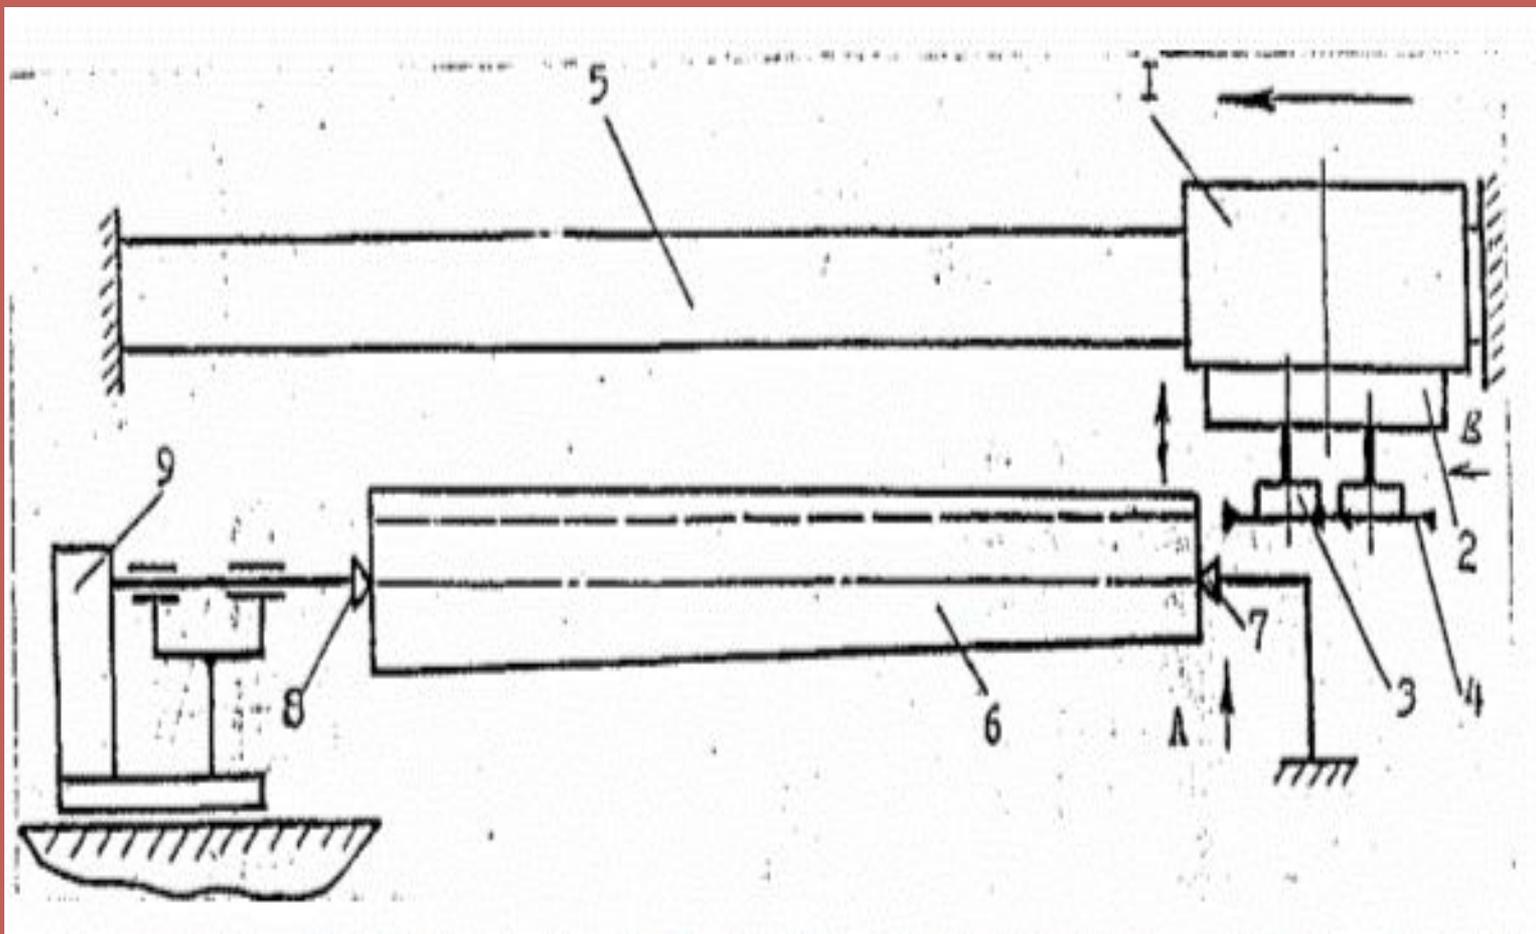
Вид А ОЦ : 1- каретка: 2- суппорт: 3- фреза: 4- пила: 6- бревно: 7- торцовый упор.
